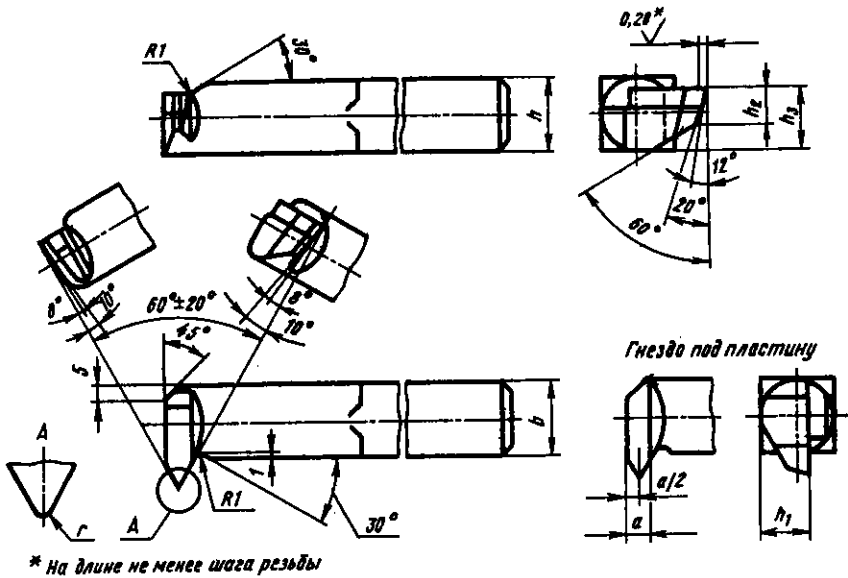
Размеры гнезда под пластину резцовых резцов для внутренних резьб
